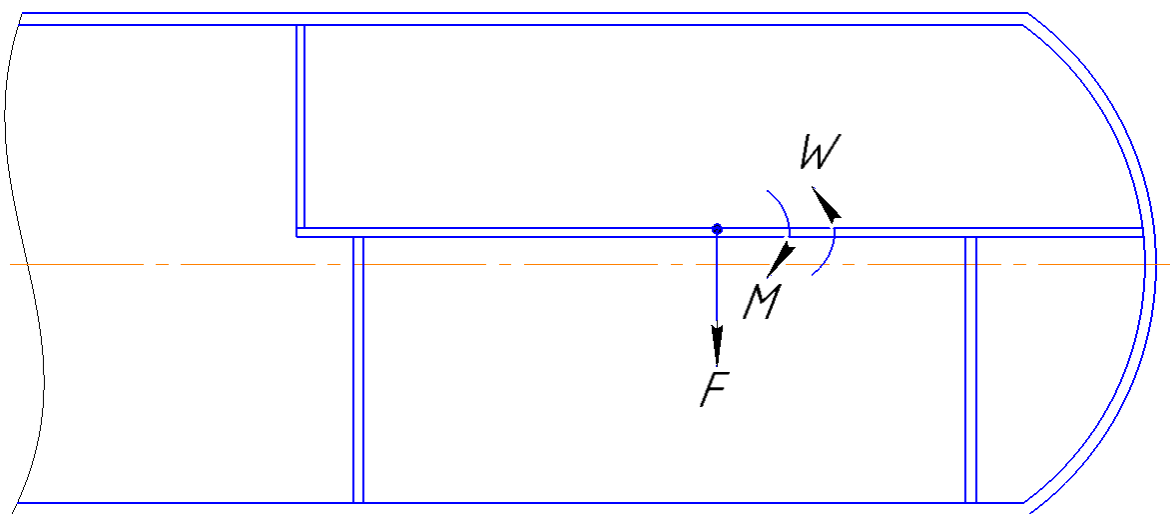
Расчетная схема сварного шва опоры короба к полотну
